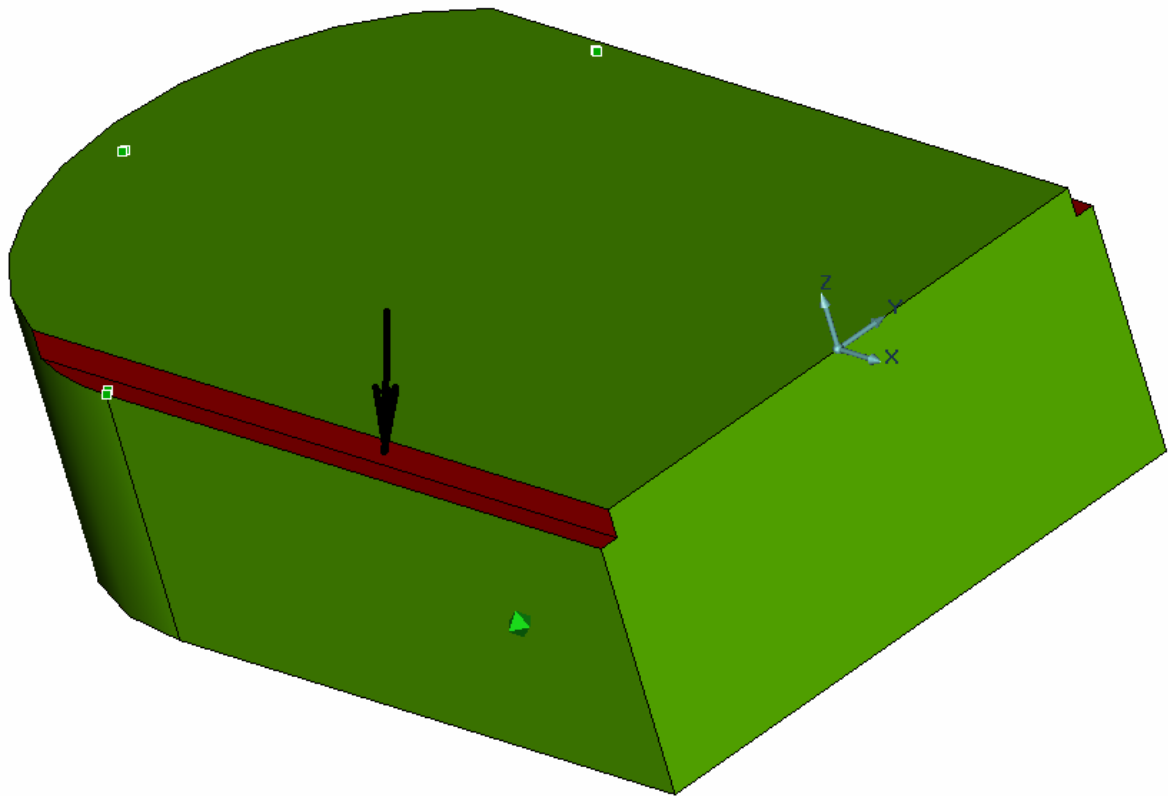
Модель обработки по предварительной фрезерной операции 005
